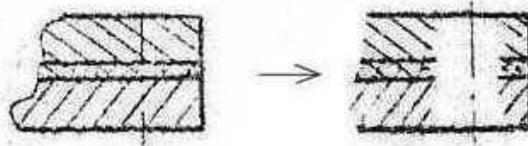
Выкопировка части изображения сборочной единицы в месте размещения болтового соединения
